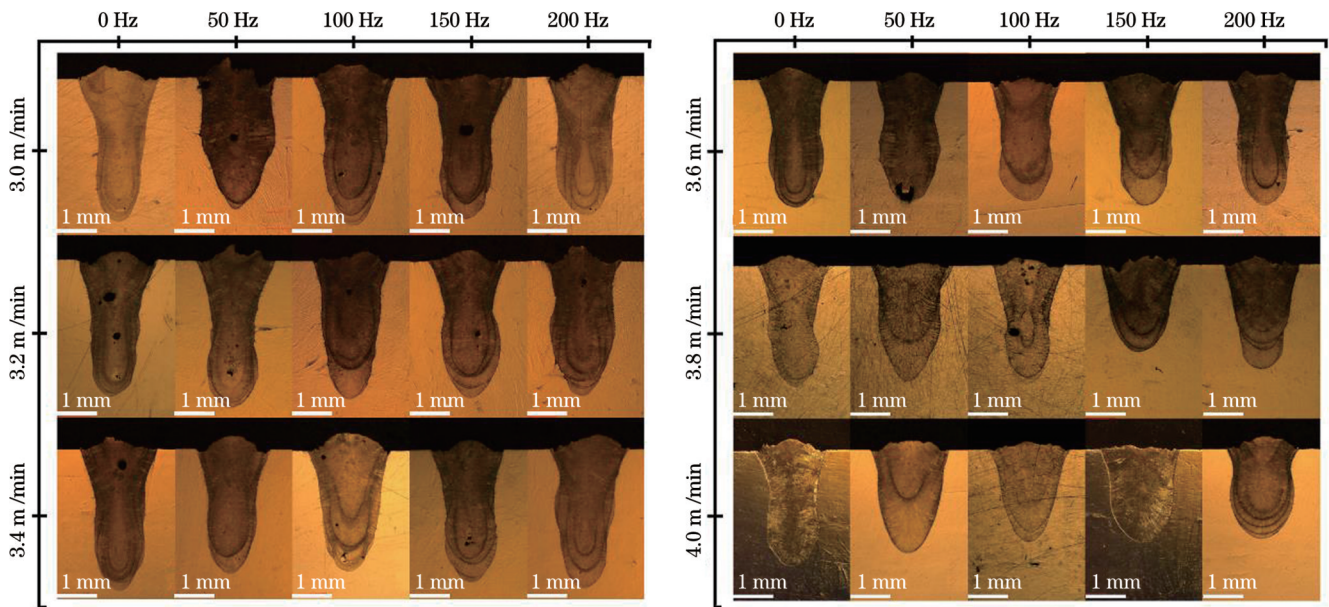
不同焊接速度和激光功率调制频率下的焊缝横截面
